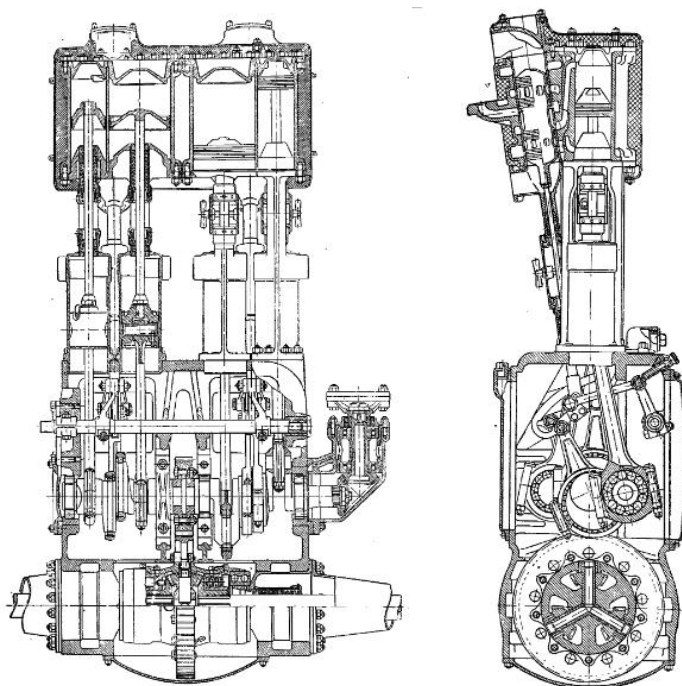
4-цилиндровый паровой двигатель автомобиля Doble Model E
